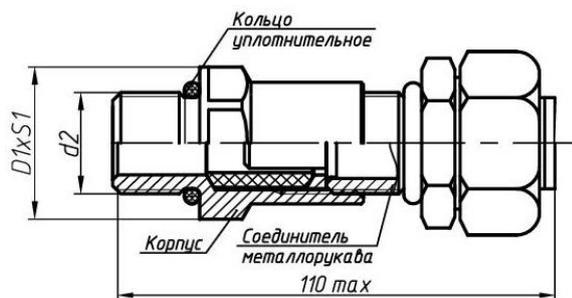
(А.29)- ЕхdКВУ-М с соединителем металлорукава Герда-СГ с наружной резьбой. Размеры см. в таблице Е.8(А.8)
